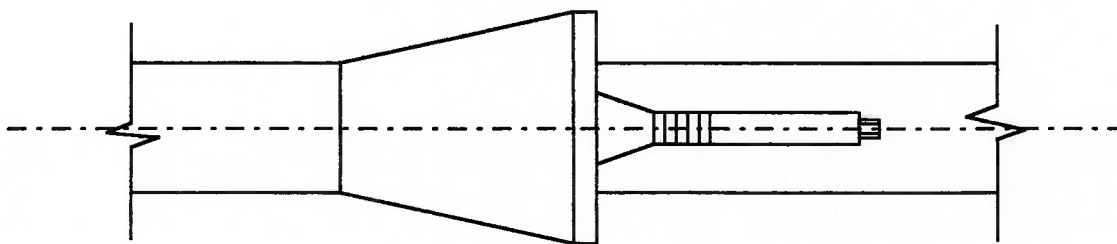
Vista superior do conjunto transdutor-adaptador-tubo
